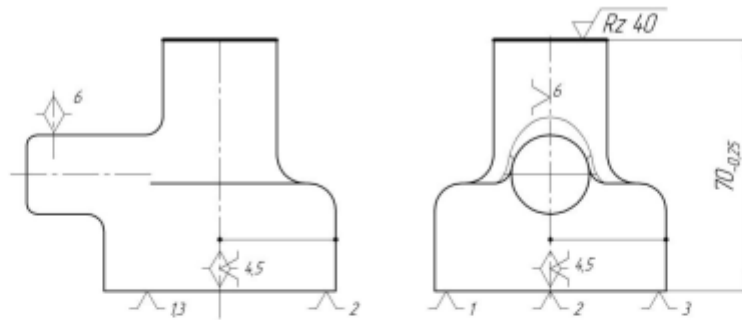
Теоретична схема базування заготовки на операції 010
